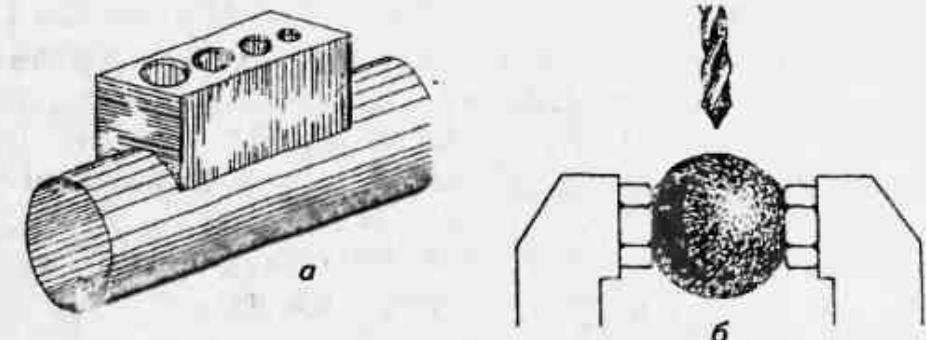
Приспособления для сверления металла: а — специальный кондуктор с серией отверстий под наиболее употребляемые сверла; б — закрепление в тисках металлического шарика
